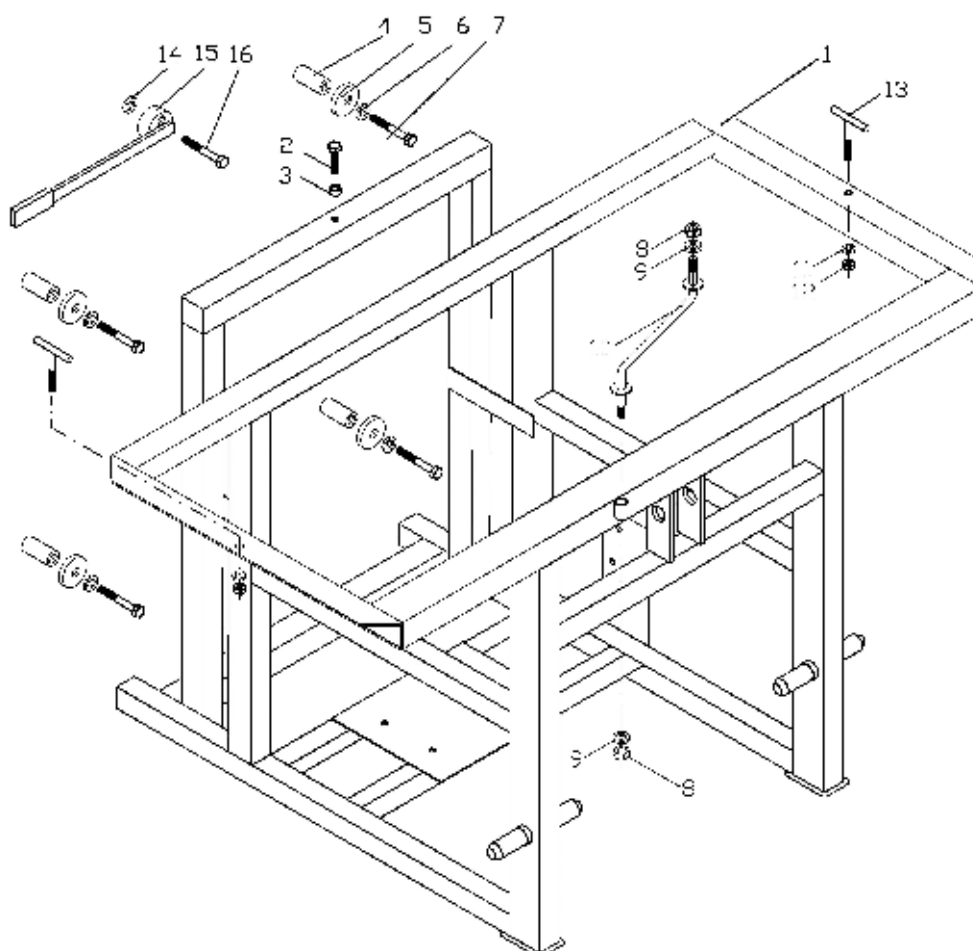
Рама опрыскивателя 600, 800 и 1000
